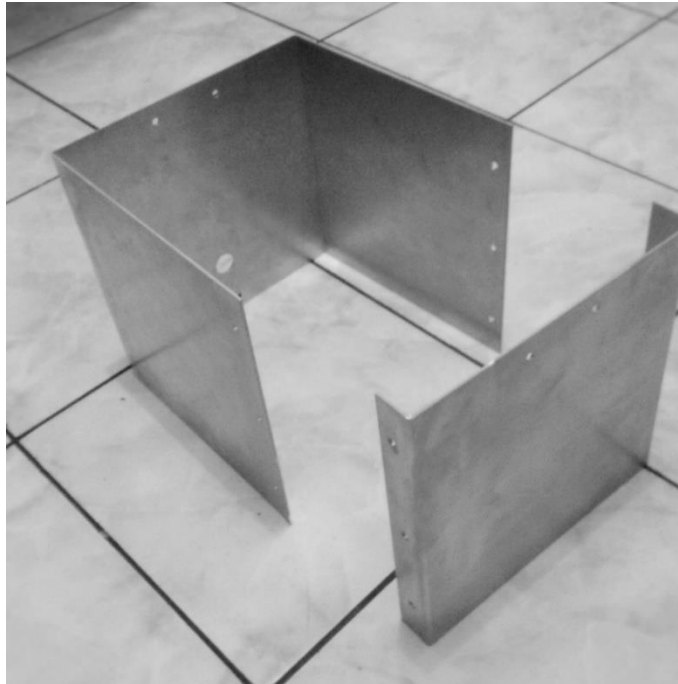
Estrutura do aparato de ensaio Jominy desmontado.
